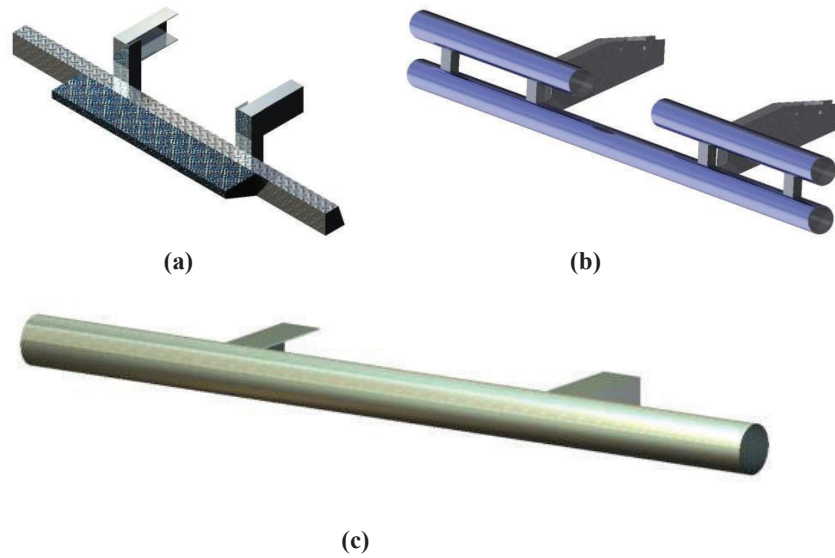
Sistemas antiempotramiento. (a) Dispositivo antiempotramiento de plancha corrugada tipo grada; (b) Dispositivo antiempotramiento de doble tubo; (c) Dispositivo antiempotramiento de un solo tubo.
